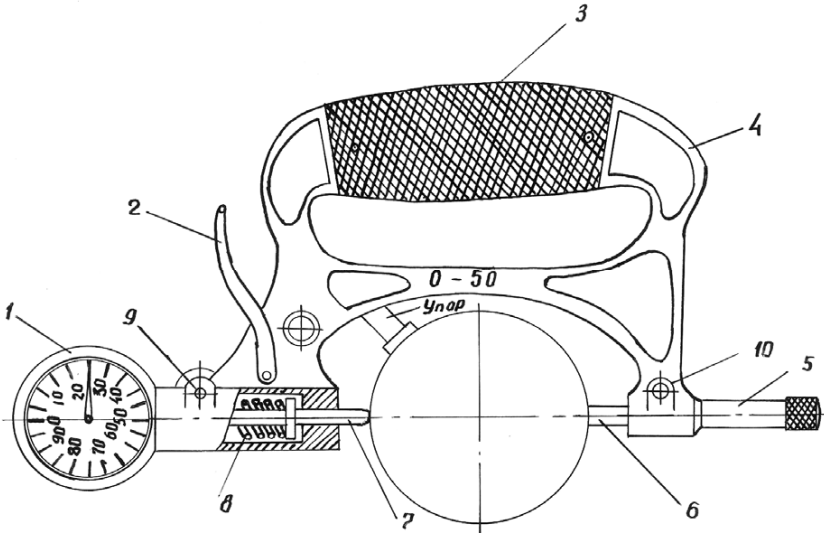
Індикатора скоба: 1 – індикатор; 2 – відводка; 3 – теплоізоляційна накладка; 4 – корпус; 5 – ковпачок; 6 – переставна п'ятка; 7 – рухома п'ятка; 8 – пружина; 9 – гвинт; 10 – затискач
